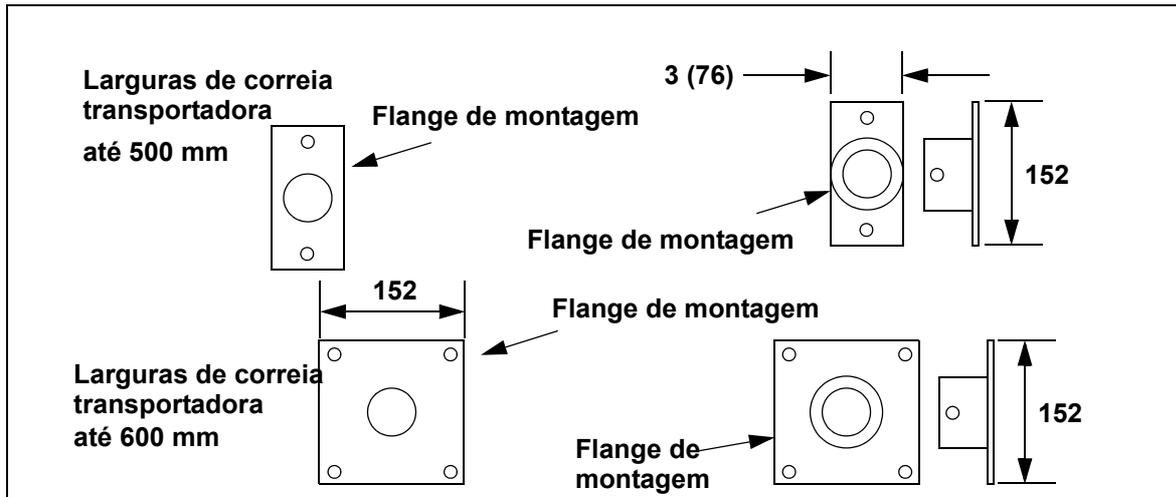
Flange de montagem do raspador em V MARTIN® TORSION ARM™
